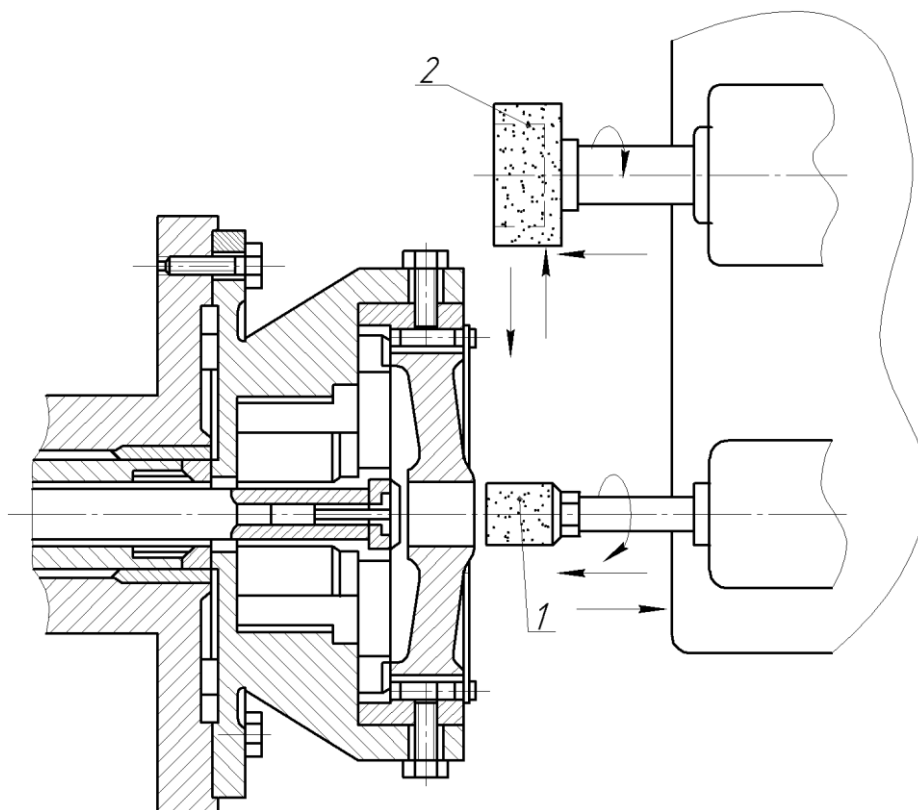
Схема шліфування отвору і торця зубчастого колеса з одного встановлення
